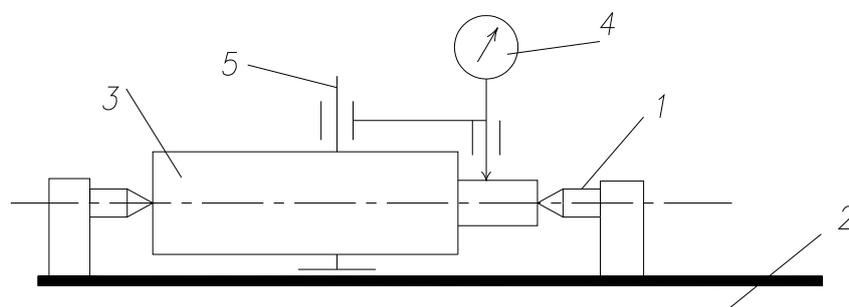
Схема опытной установки для определения геометрических отклонений шейки вала
